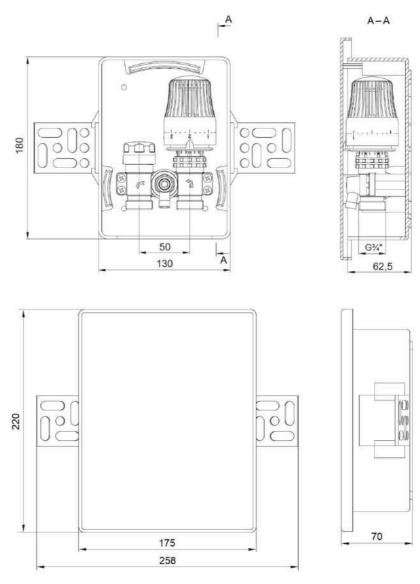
Габаритные размеры регулировочного короба Oks00730
